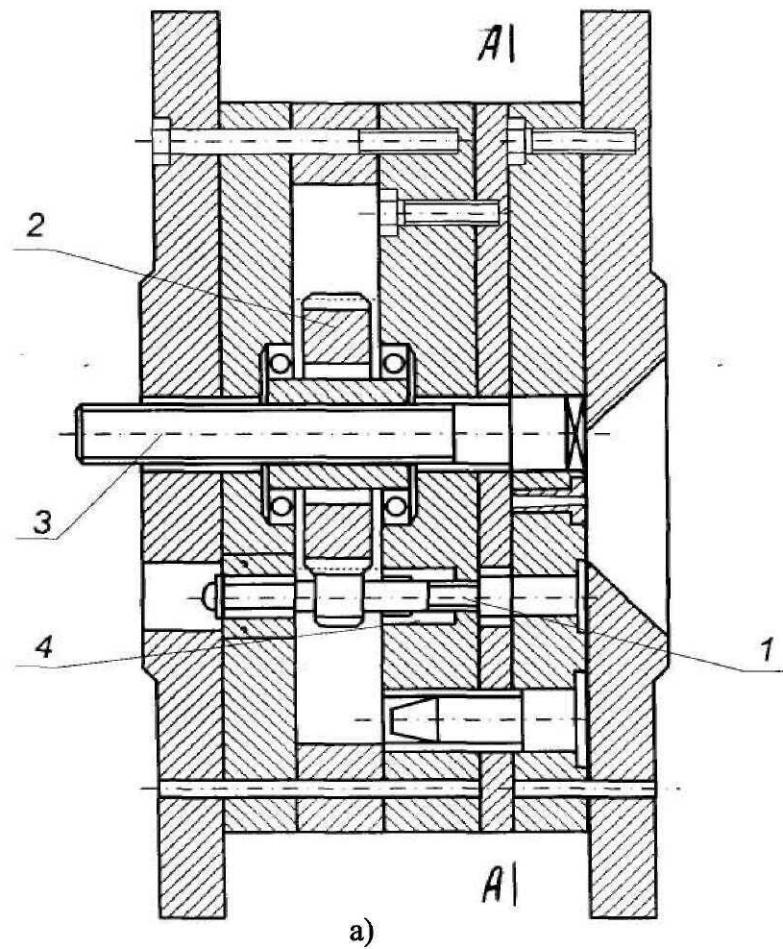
Пресс-форма для изготовления деталей с внутренней резьбой:
